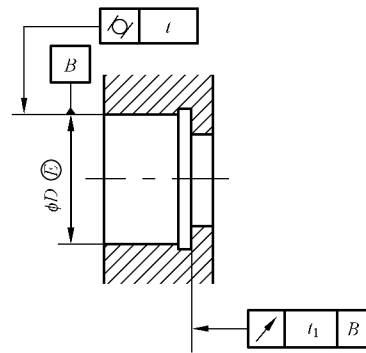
轴承座孔表面的圆柱度公差和孔肩的轴向圆跳动
